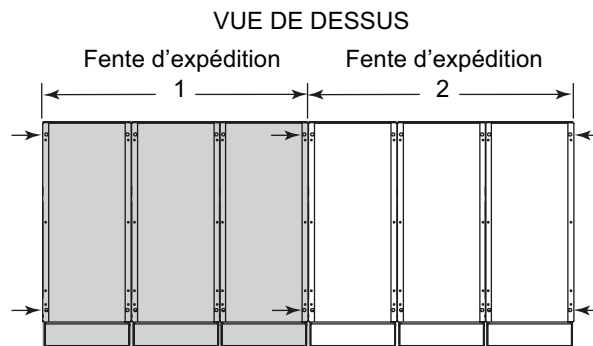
Assemblage des unités d'expédition et installation des panneaux d'extrémité
